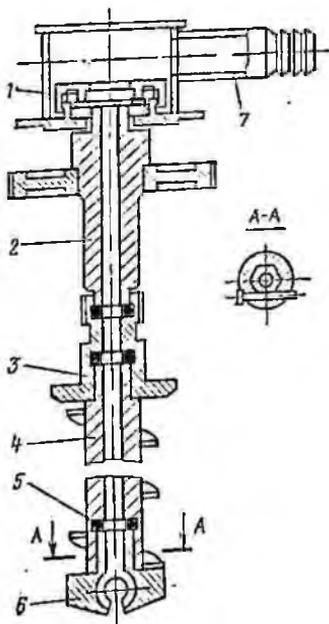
Схема подвода воздуха для шнекопневматической очистки скважин: 1—система подачи сжатого воздуха; 2—вращатель; 3—вольный шпиндель; 4—буровые шнеки; 5—уплотнение; 6—долото; 7—штуцер для подачи сжатого воздуха
